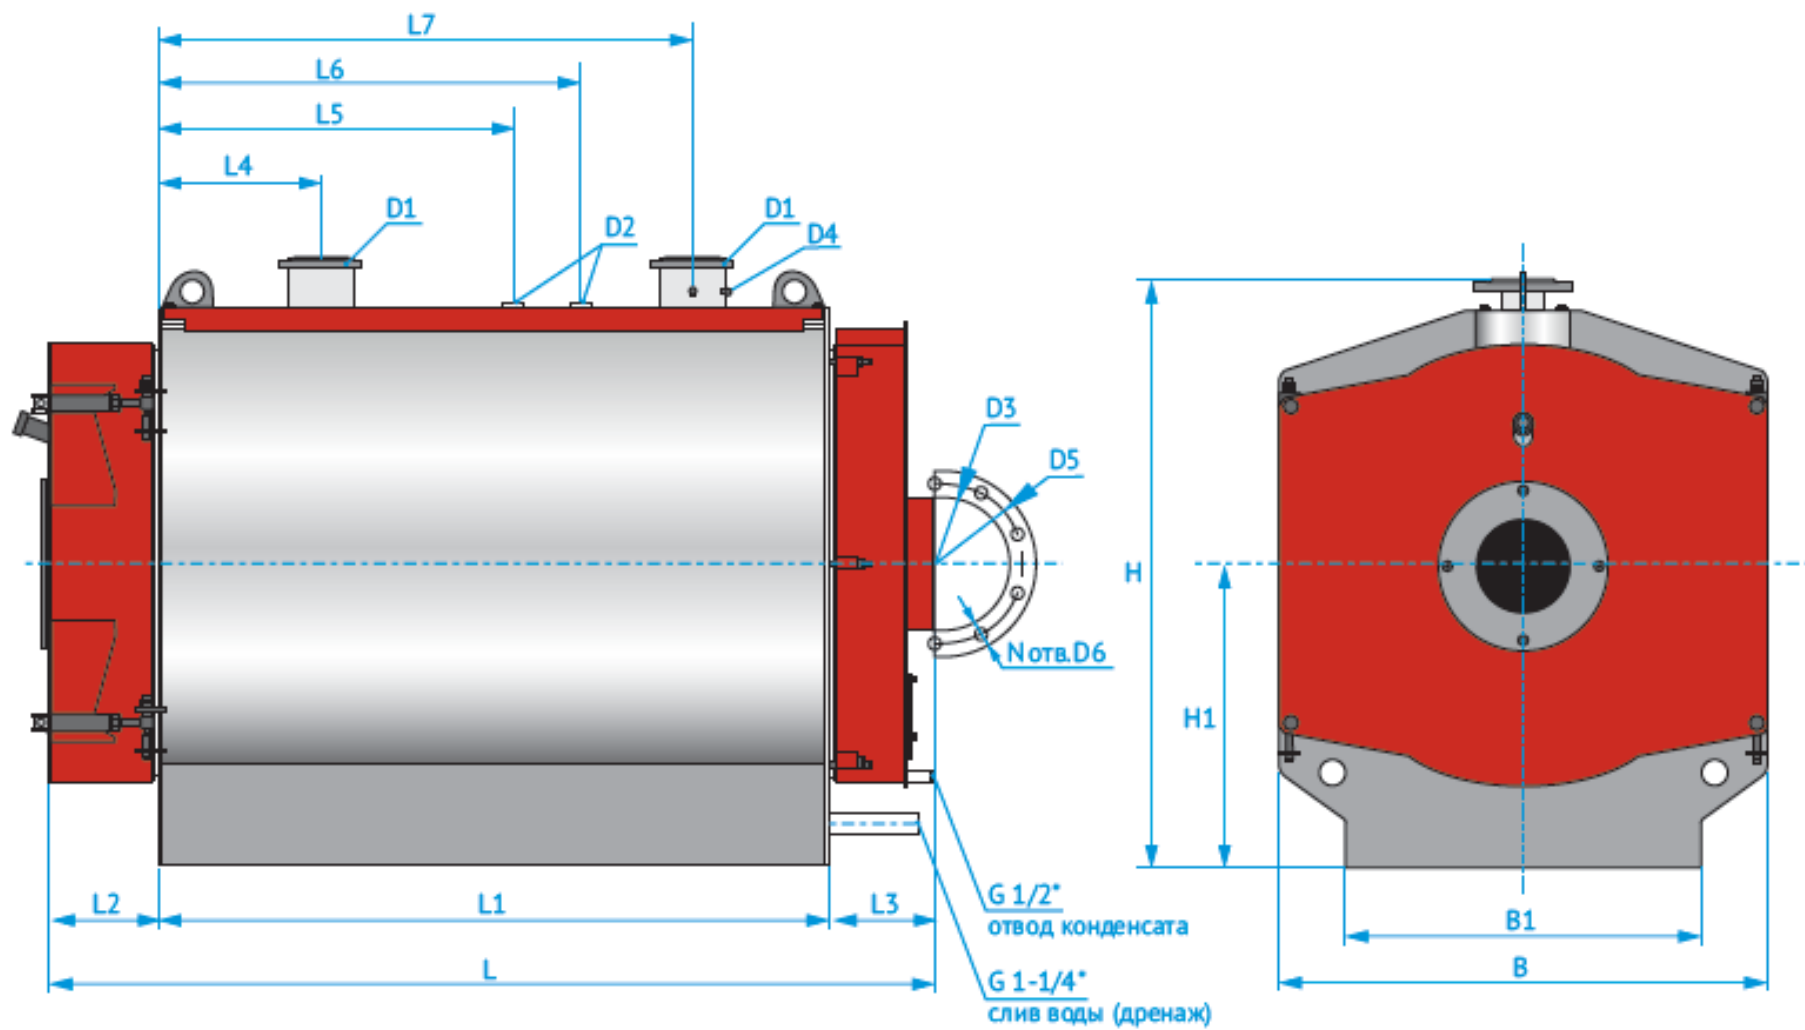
Габаритные и присоединительные размеры котлов WL1500-6000
